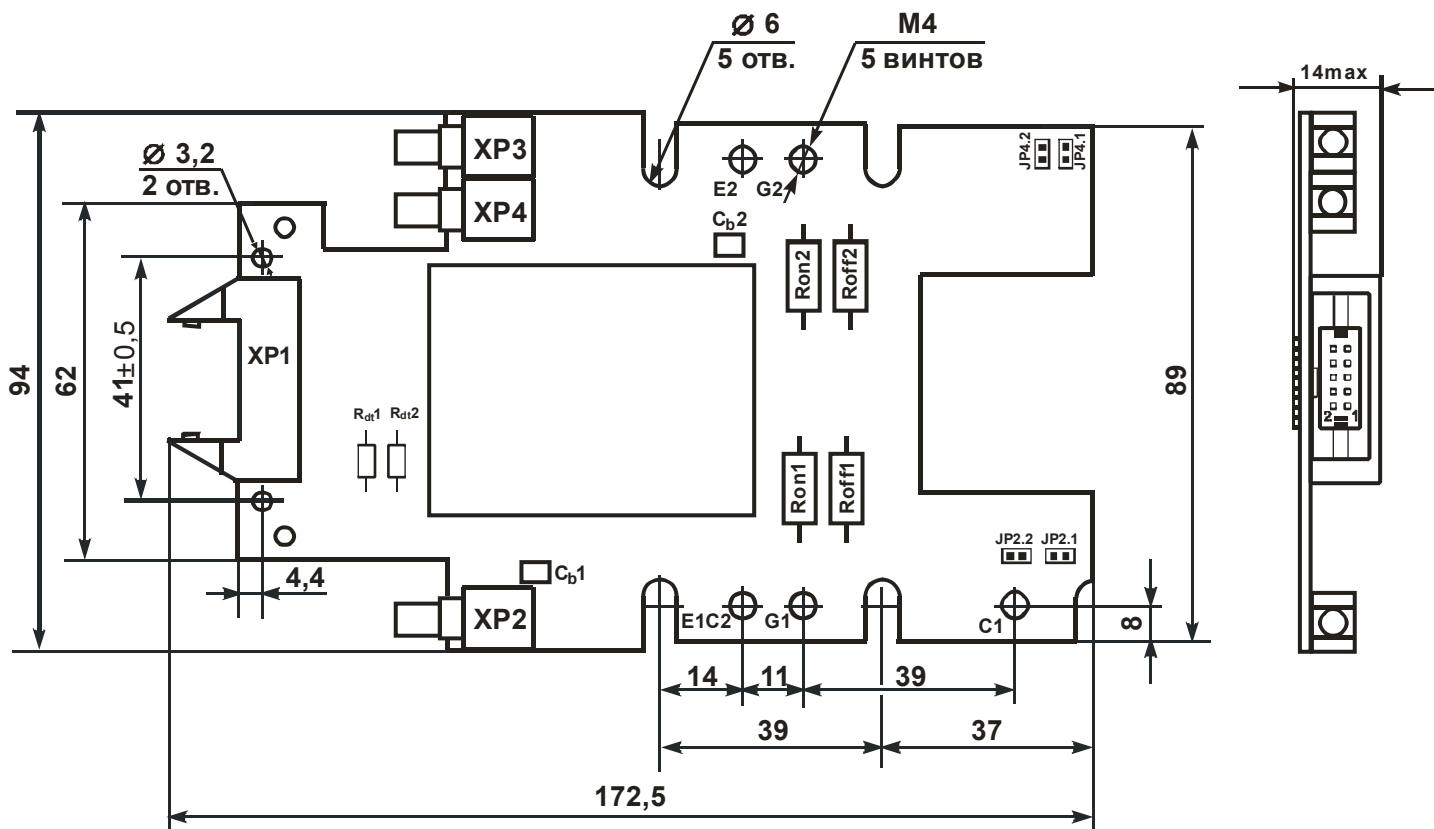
Габаритный чертёж драйвера ДР2180П-БВ1-2
